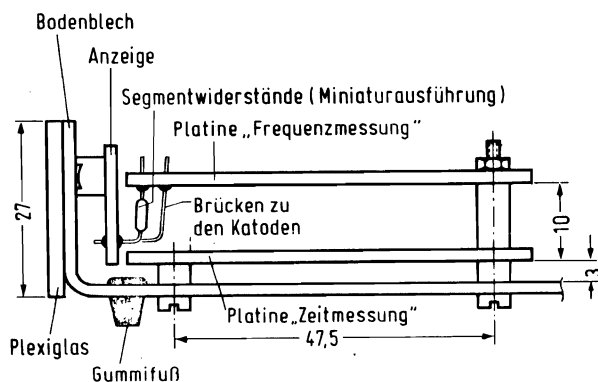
Detailzeichnung und Maßangaben (in mm) für den mechanischen Zusammenbau der Platinen (Seitenansicht)
